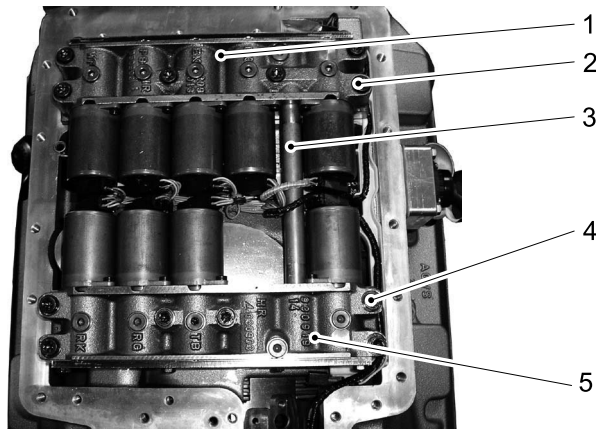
1 – Steuerblock; 2 – Schrauben; 3 – Verbindungsrohr; 4 – Steuerblock
